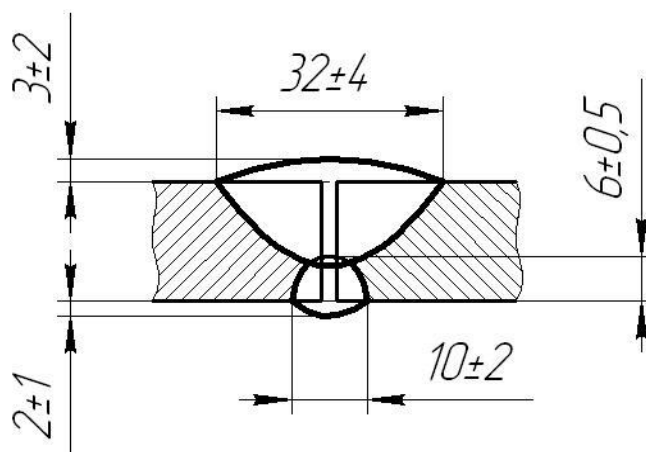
Геометрические параметры сварного шва после автоматической сварки под флюсом
